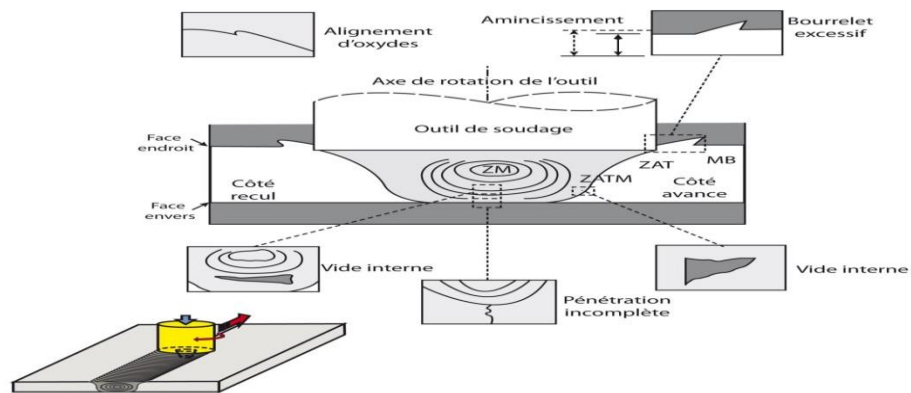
Schéma montrant la position des défauts en soudage FSW en soudure bout à bout. [1]
